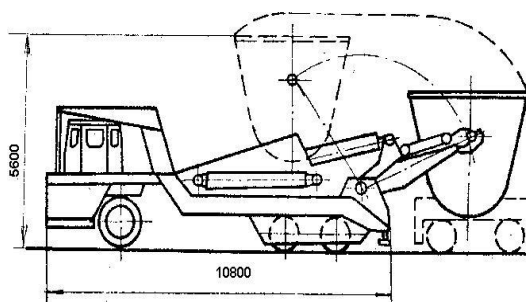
Автошлаковоз. Схема перестановки шлаковой чаши
